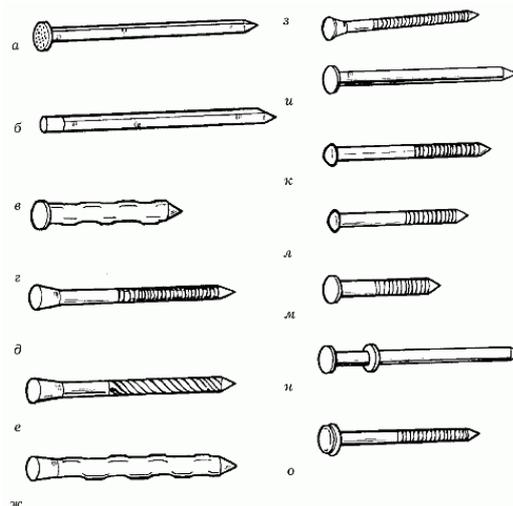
Типы гвоздей: а – гвоздь прямой, гладкий, четырехгранный, с оцинкованной или простой поверхностью для строительных и плотничных работ; б – гвоздь дюкерный, четырехгранный, не имеющий головки; в – гвоздь для кровли, круглый профилированный, используется при работе с картоном, толем и т. д.; г – гвоздь ребристый, круглый с рифленой оцинкованной поверхностью, необходим для соединений с большими нагрузками на растяжение; д – гвоздь крученный, имеющий обычную или потайную головку, применяется в местах с изменяющейся нагрузкой (доски полов); е – гвоздь с ребристой профилированной поверхностью; ж – гвоздь с увеличенной шляпкой в форме шайбы, круглый с ребристой поверхностью, используется с дополнительной уплотняющей шайбой для укрепления кровли; з – гвоздь анкерный, круглый с оцинкованной ребристой поверхностью; и – гвоздь твердый, стальной, используется при работе с бетоном; к – гвоздь круглый, кислотоупорный со скругленной шляпкой и ребристой поверхностью, применяется в местах, подверженных коррозии; л – гвоздь медный или бронзовый, панельный с ребристой поверхностью и декоративной шляпкой, используется в местах с высокой влажностью; м – гвоздь круглый с оцинкованной рифленой поверхностью и широкой шляпкой, применяется при работе с битумными плитами; н – гвоздь с двойной шляпкой, используется там, где он впоследствии будет удален, например в опалубках; о – гвоздь круглый, кровельный с оцинкованной рифленой поверхностью и со скругленной шляпкой, имеющей уплотнитель, используется при креплении облицовочных или кровельных профилированных плит.
